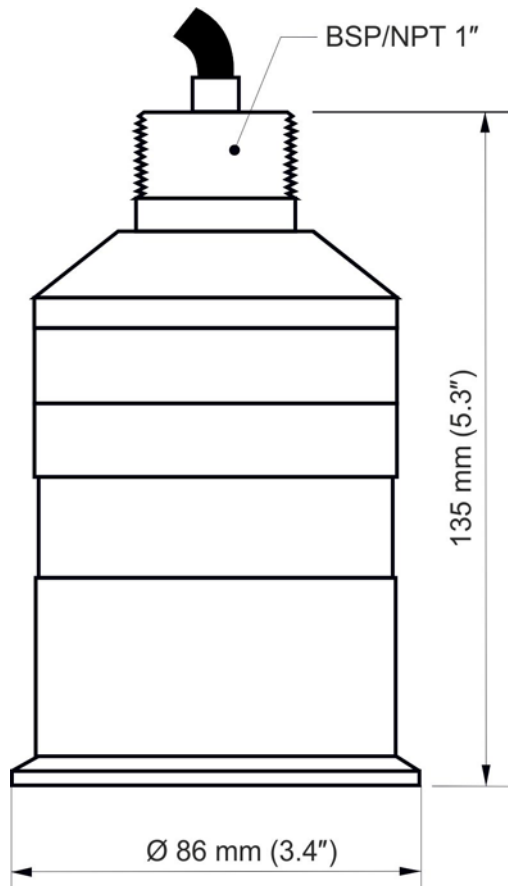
Abmessungen i-Sensor Typ 15 mit Einbaugewinde kabelseitig
